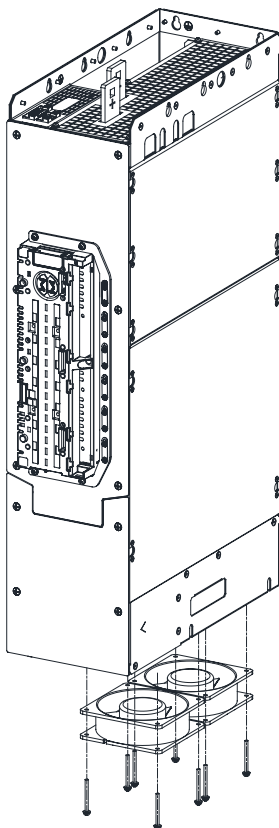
Замена вентилятора инверторного блока типоразмера Н6...Н7
